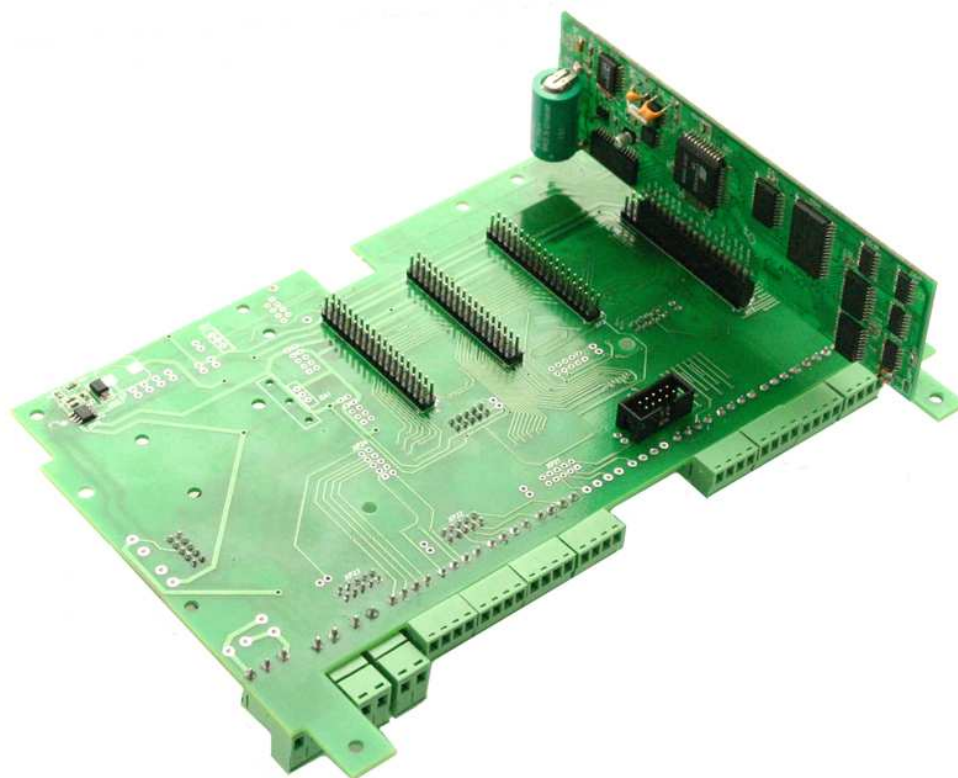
Установка платы ЦП на базовую плату контроллера
